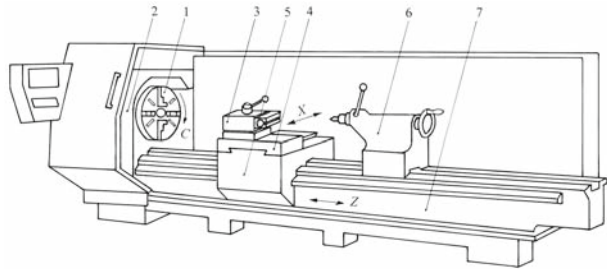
Präzisions-Drehmaschine mit Zyklenautomatik für schwere Werkstücke (Weiler)
